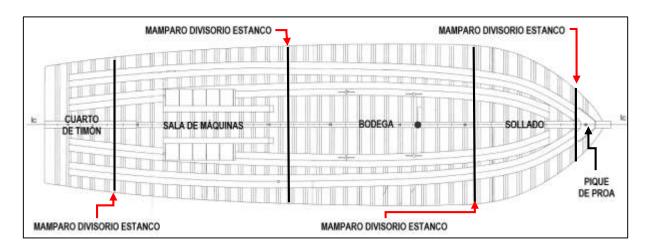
Ubicación de mamparos y secciones en plano constructivo longitudinal. Fuente: material documental
